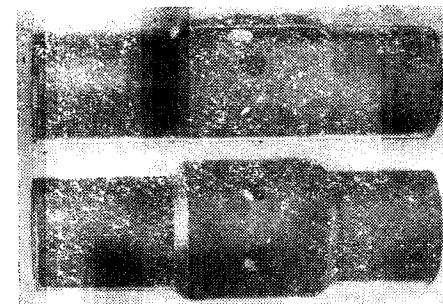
Пробивка отверстий с помощью полиуретана [18]:
